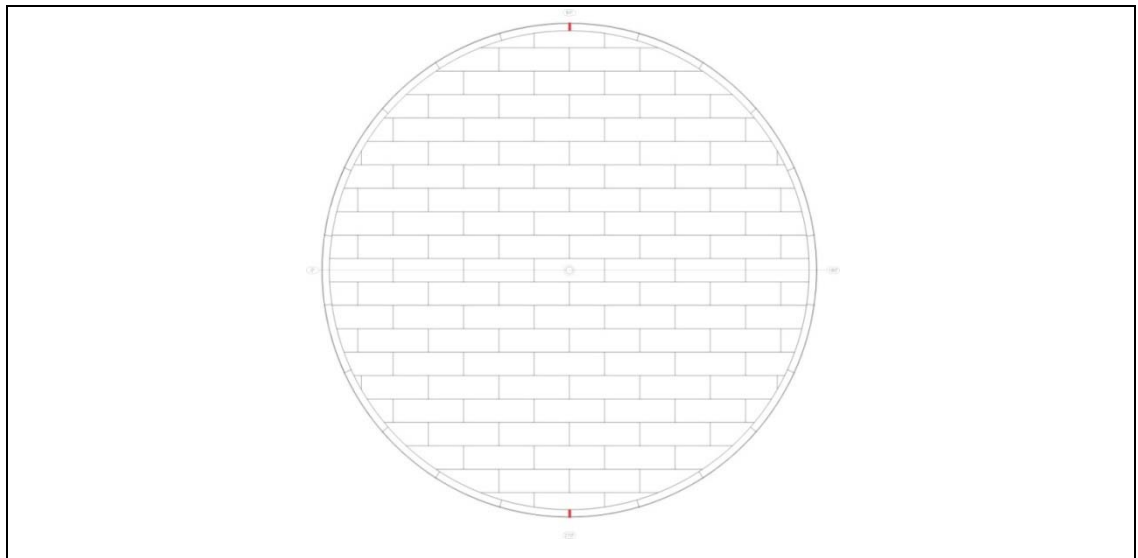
Juntas que serão soldadas por último. Autores
